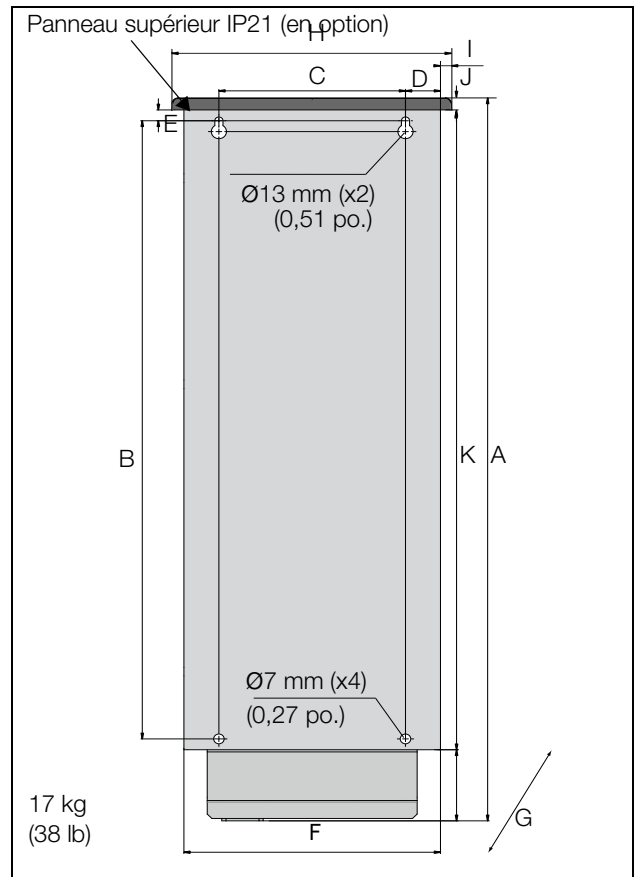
Emotron FDU modèle 48-025 à 48-058 (taille de châssis C2), Modèles 69-002 à 69-025 (taille de châssis C2(69)), vue arrière.
